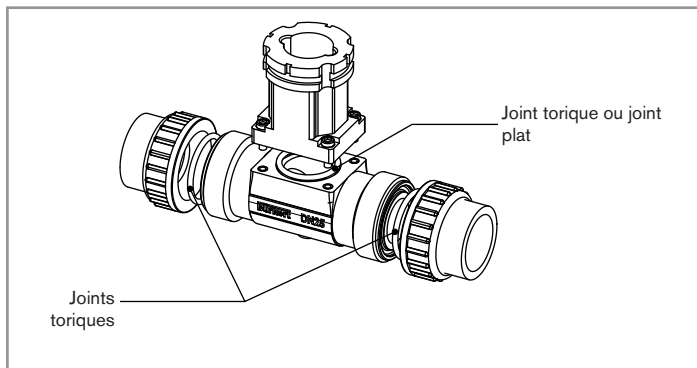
Joints d'un raccord en T avec embouts union à coller ou à souder
